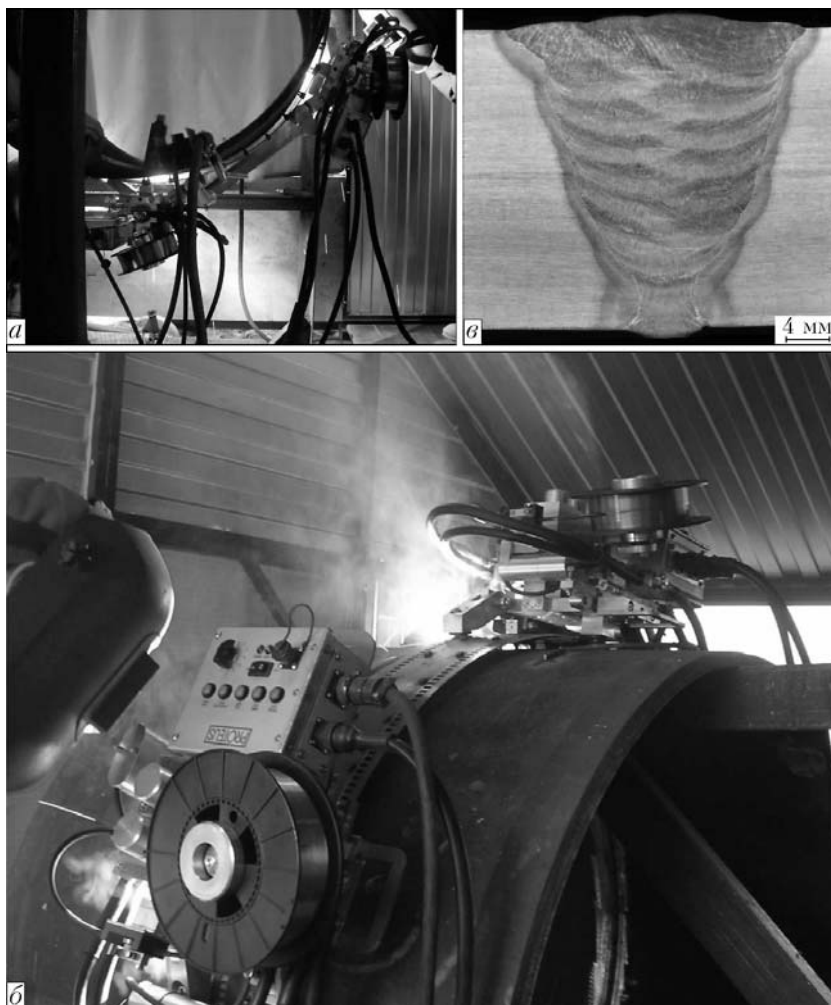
Начало (а) и конец (б) процесса автоматической сварки неповоротного стыка трубопроводов на комплексе «ПРОТЕУС» и шлиф сварного соединения трубопровода из стали К65 толщиной 27,7 мм (в)
